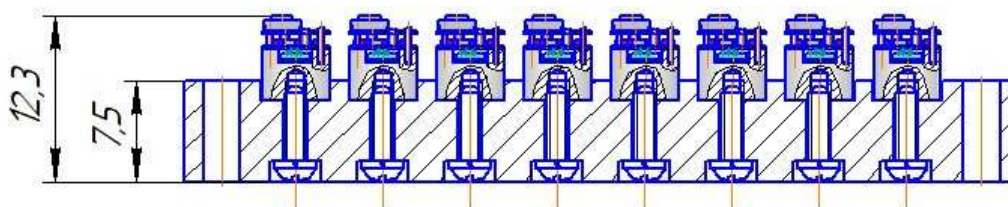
Эскиз основания-радиатора с установленными сборочными единицами
